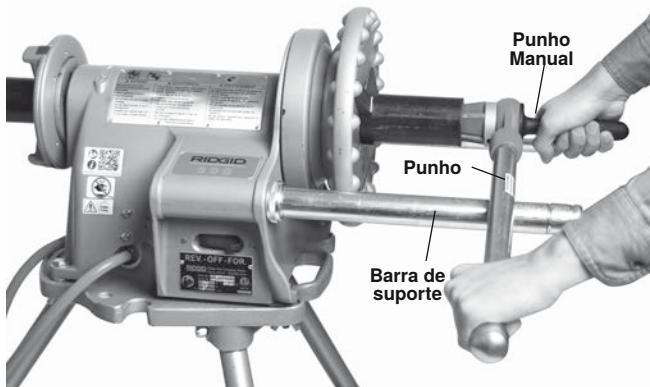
Escareador de tubos com escareador manual (manter o cabo do escareador em contacto com a barra de suporte)
